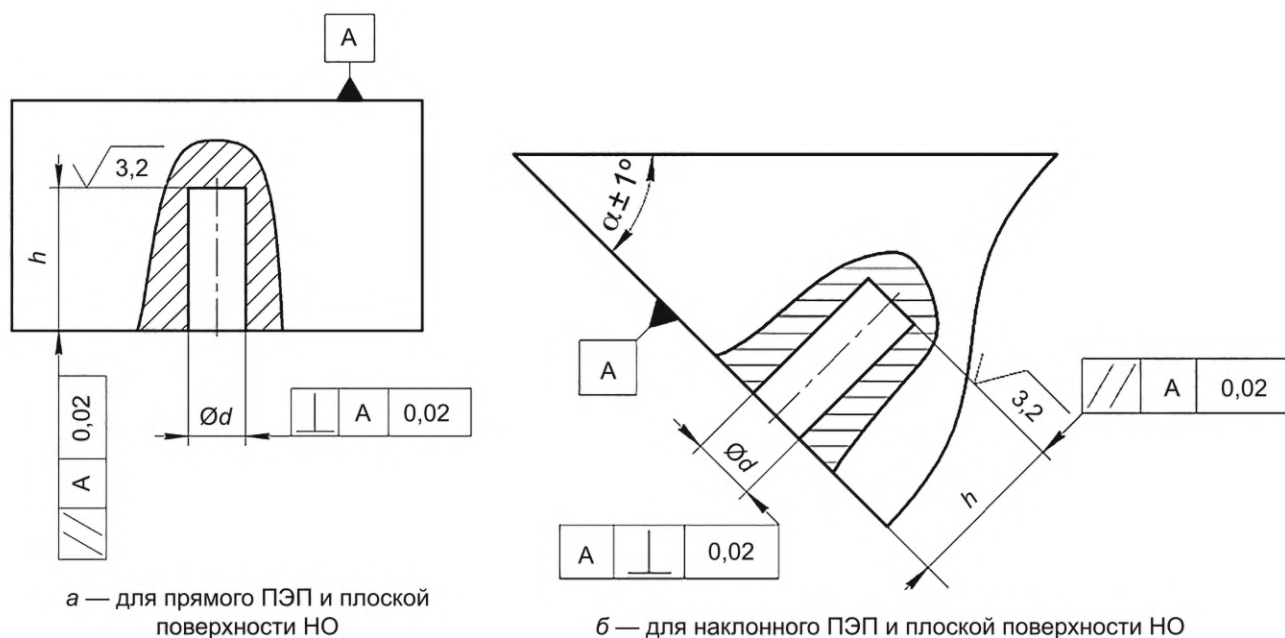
Допуски на изготовление ПДО
